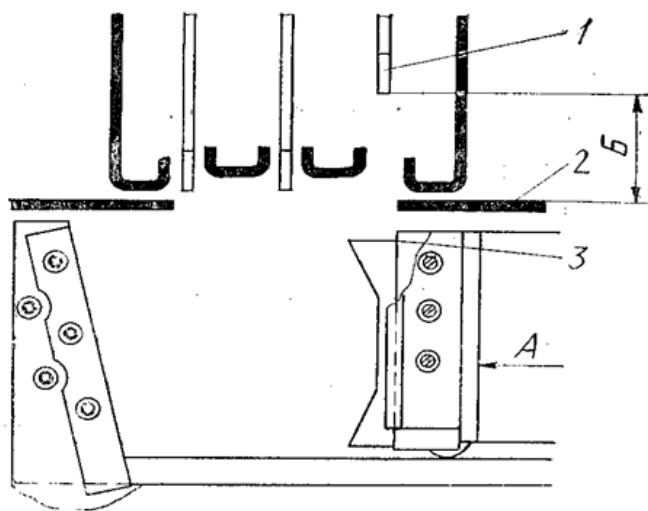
Положение зубьев переднего упаковщика и поршня: 1-короткий зуб упаковщика; 2-крыша прессовальной камеры; 3-лобовина поршня; А-рабочий ход поршня; Б = 70...100 мм.
